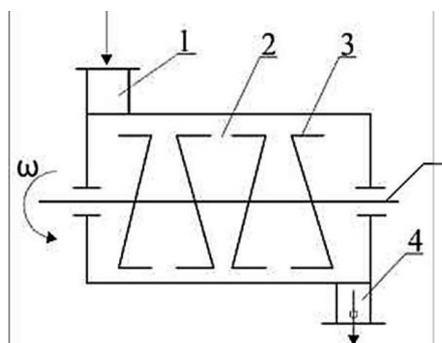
Схема лопастного горизонтального смесителя: 1 – загрузочное устройство; 2 – корпус; 3 – лопасть; 4 – выпускное устройство; 5 – вал
